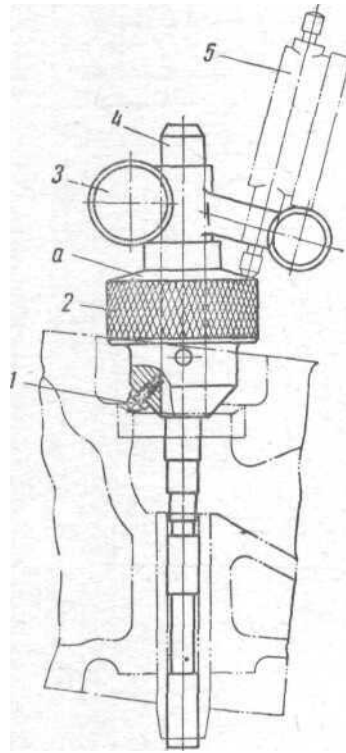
Приспособление для проверки concentричности фаски седла клапана относительно направляющей втулки
